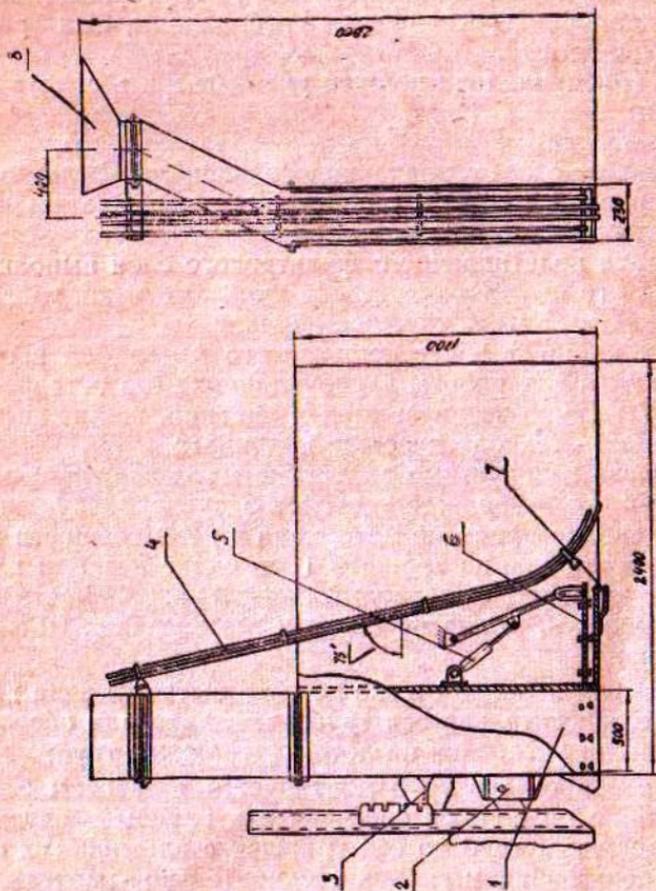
Схема навесного трубоподдерживающего к ЭТЦ-163 для укладки
